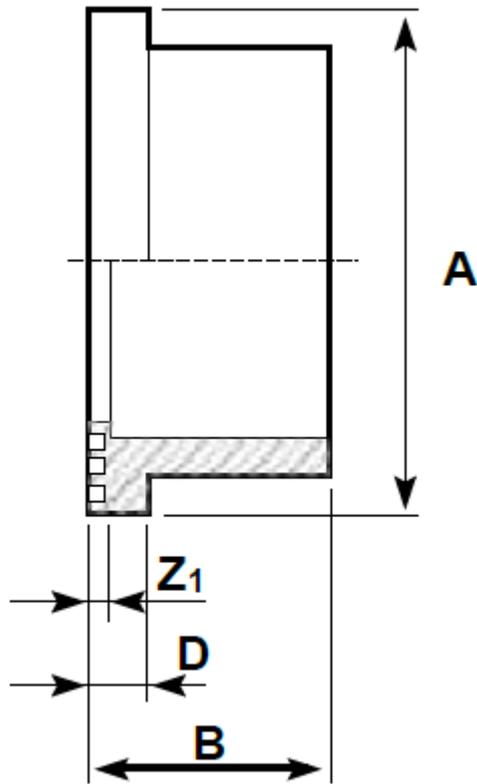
Муфта разъемная с внутренней резьбой из нержавеющей стали
